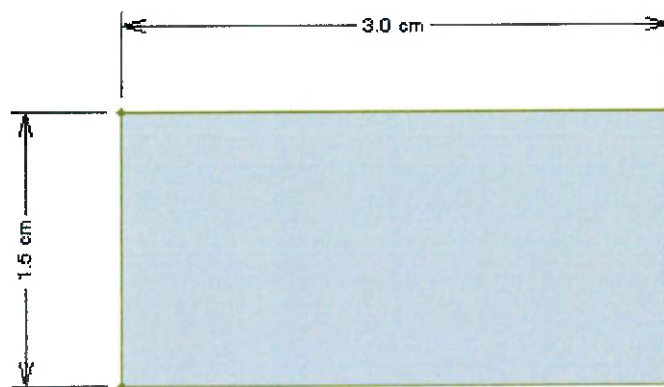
Seção transversal barra de fixação do eixo dianteiro
